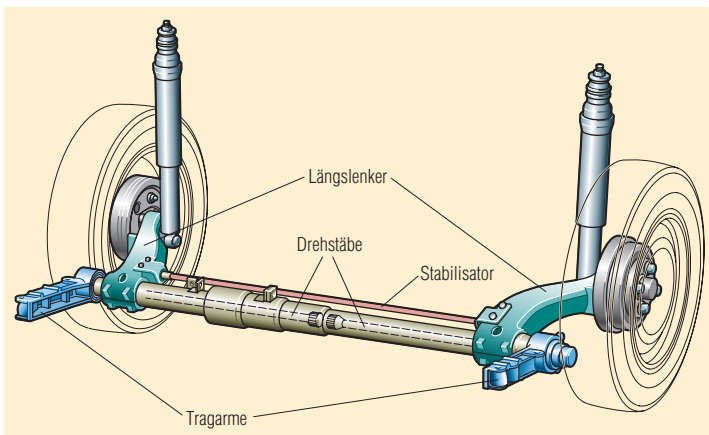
Längslenkerachse mit Drehstabfederung.
